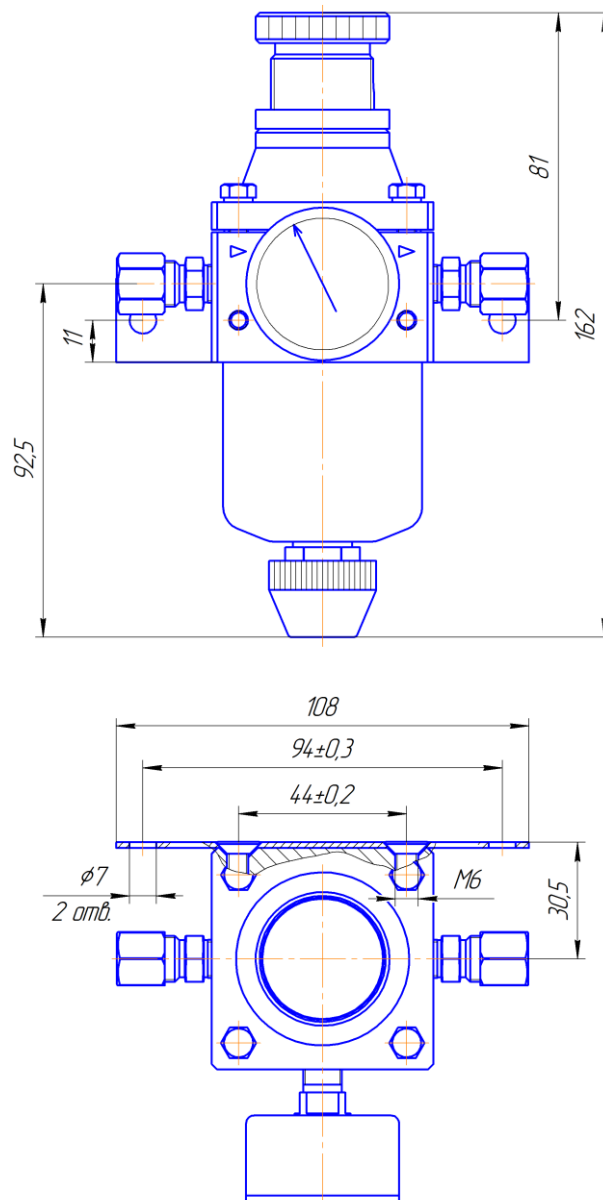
Габаритные и присоединительные размеры редуктора РДФ-01М
